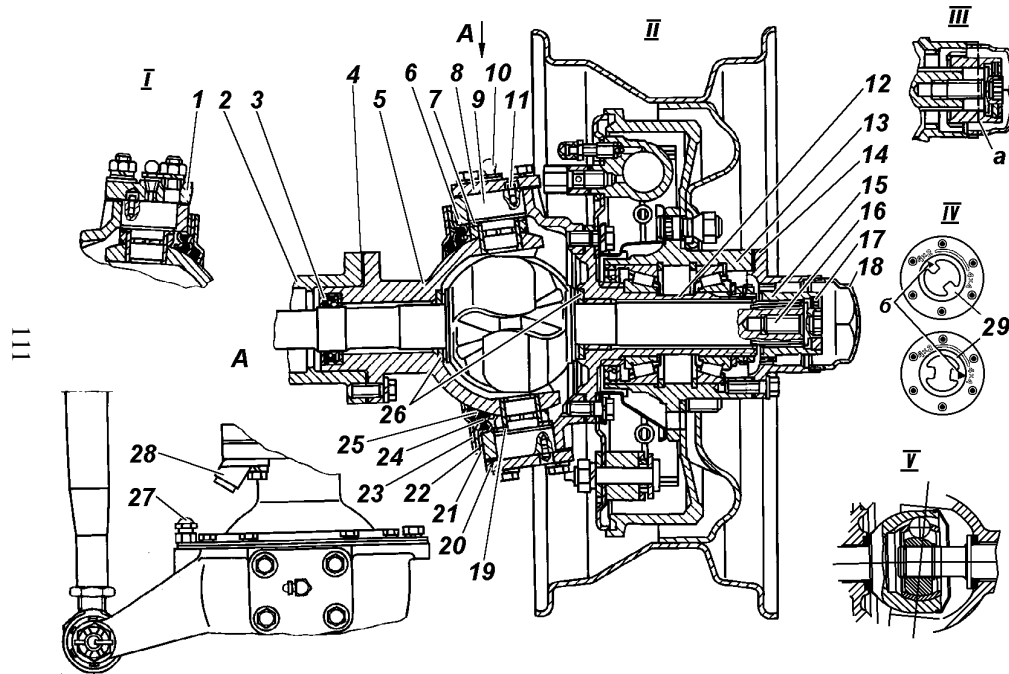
Поворотный кулак автомобилей УАЗ-31512, УАЗ-31514, УАЗ-31519: а -сигнальная канавка; б -указатель; I - правый поворотный кулак; II - левый поворотный кулак; III - муфта отключения колес; IV - муфта отключения колес; V - шарнир типа "Бирфильд" (вариантное исполнение); 1 -рычаг поворотного кулака; 2 -кожух поворотного кулака; 3 -сальник; 4, 20 - прокладки; 5 -шаровая опора; 6 -корпус поворотного кулака; 7 -опорная шайба; 8 -накладка; 9 -шкворень; 10 -пресс-масленка; 11 -стопорный штифт; 12 -цапфа; 13 -ступица колеса; 14 -ведущий фланец; 15 -муфта; 16 -болт муфты; 17 -шарик фиксатора; 18 -защитный колпак; 19 -втулка шкворня; 21 -внутренняя обойма; 22 -кольцо-перегородка; 23 -наружная обойма; 24 -резиновое уплотнительное кольцо; 25 -войлочное уплотнительное кольцо; 26 -упорные шайбы; 27 -болт ограничения поворота; 28 -упор-ограничитель поворота колеса; 29 -диск муфты
